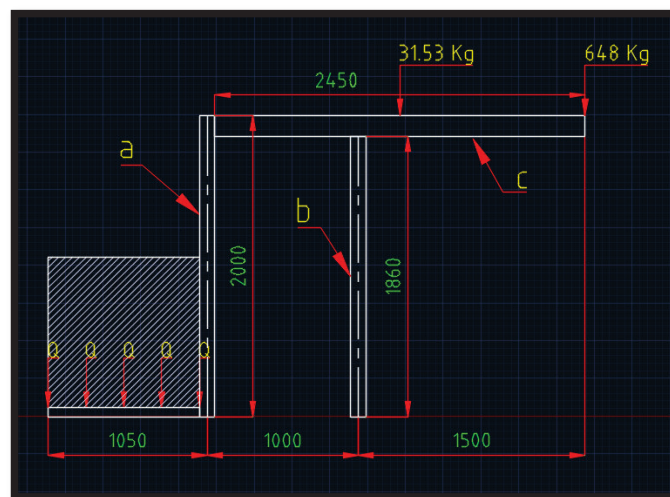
Ubicación de las cargas que actúan sobre el dispositivo
